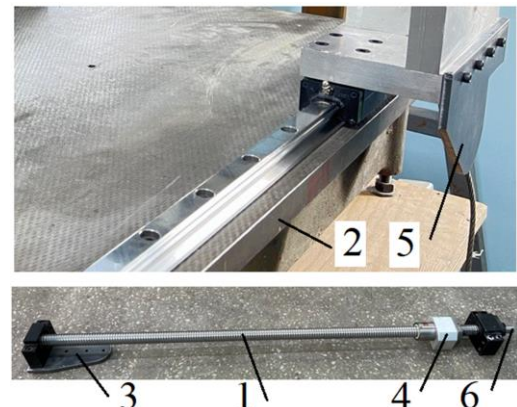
Механизм перемещения портала фрезерного 3 – D станка по оси X.
